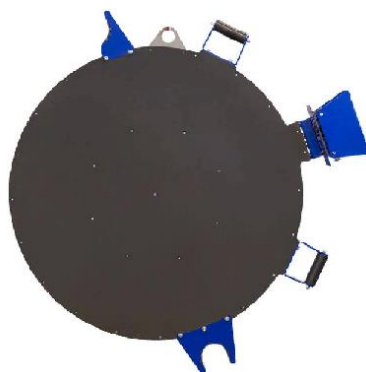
Нагревательный элемент для сварки полиэтиленовых труб
